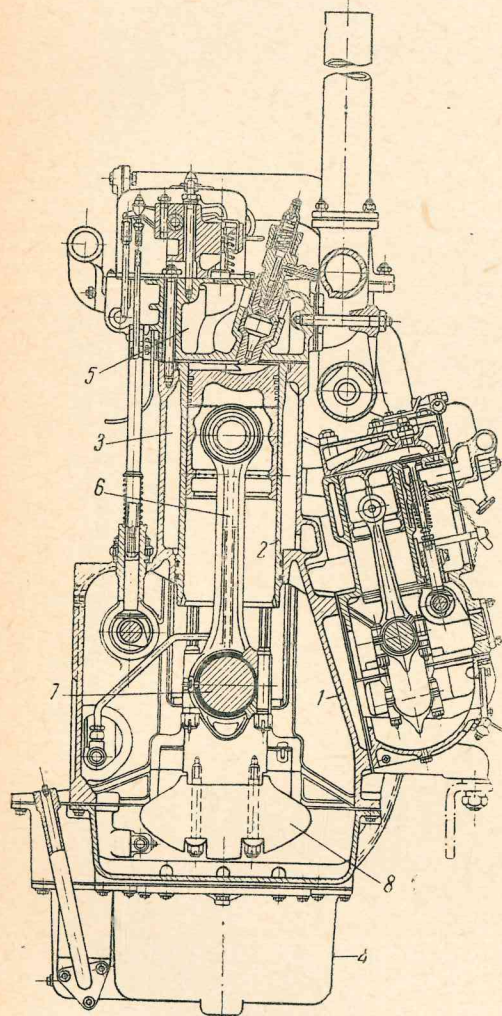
Поперечный разрез двигателя М-17: 1—картер двигателя; 2—цилиндрические гильзы; 3—водяная рубашка; 4—нижняя съемная часть картера; 5—форкамера; 6—шатун; 7—коленчатый вал; 8—чугунные противовесы
